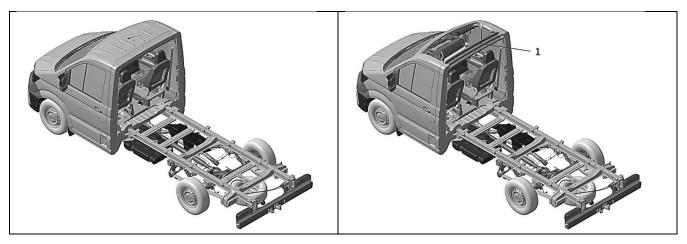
Plage d'auvent (variante avec et sans pavillon de cabine)
